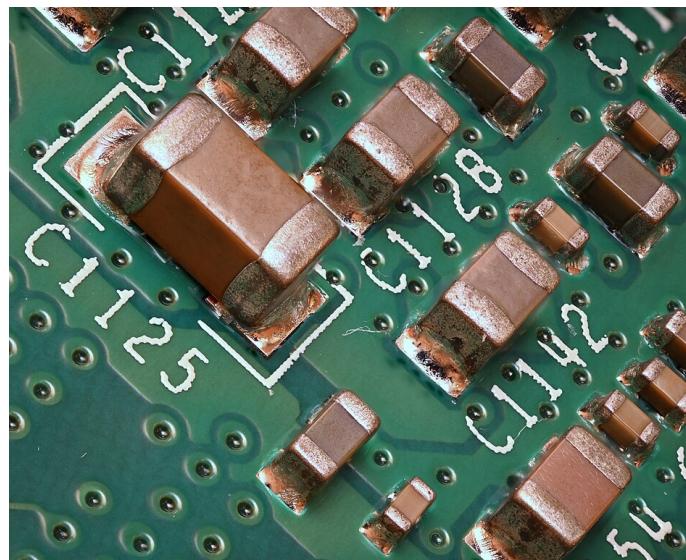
Componentes SMD unidos a la PCB con soldaduras de estaño-plomo.
